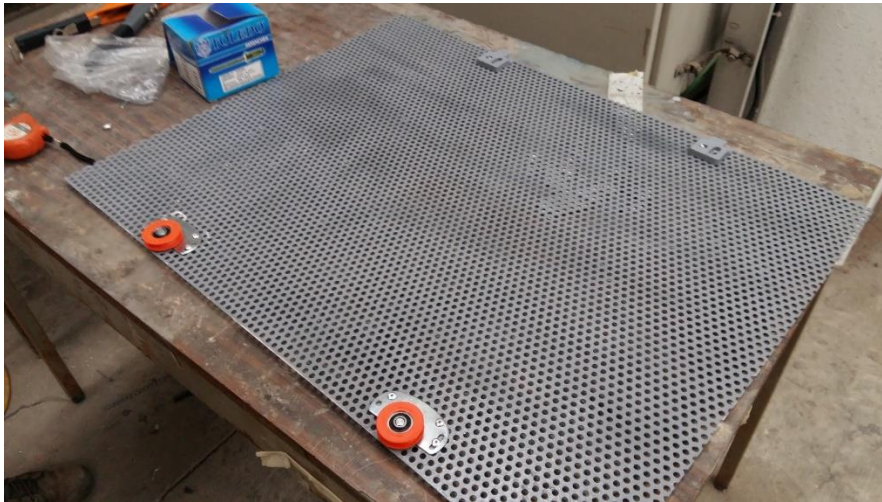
Lámina de acero al carbón con rodamientos para los carriles de aluminio
